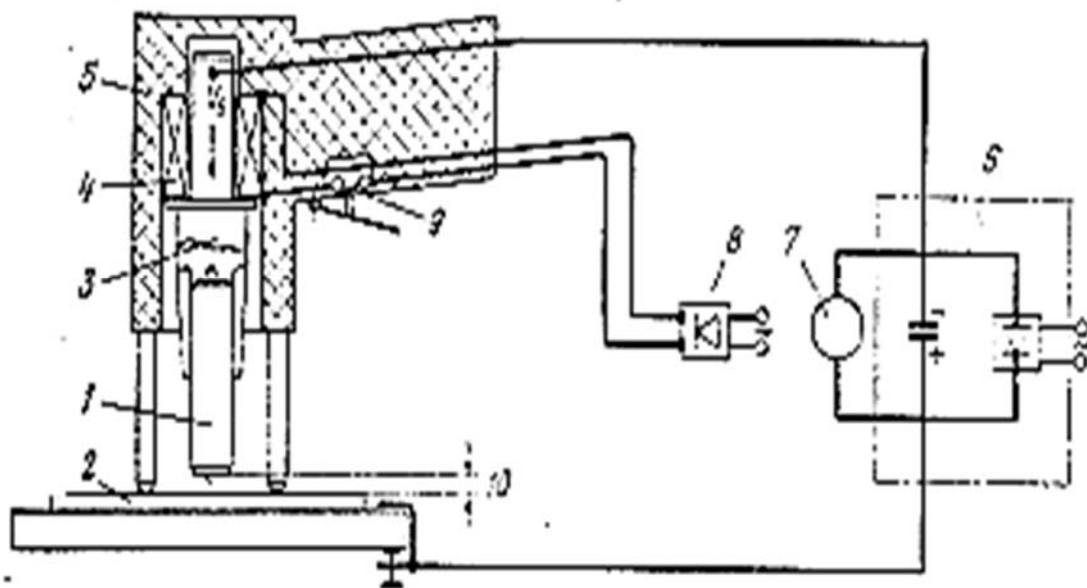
Стадии процесса ударной конденсаторной сварки шпилек
